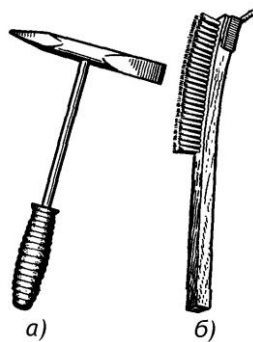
Инструмент для зачистки шва и свариваемых кромок, где а – молоток-шлакоотделитель, б – щетка
